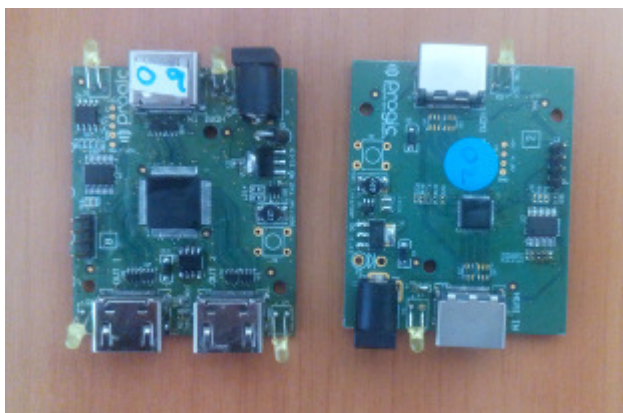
PCBs do divisor e do extensor já com os componentes soldados.
